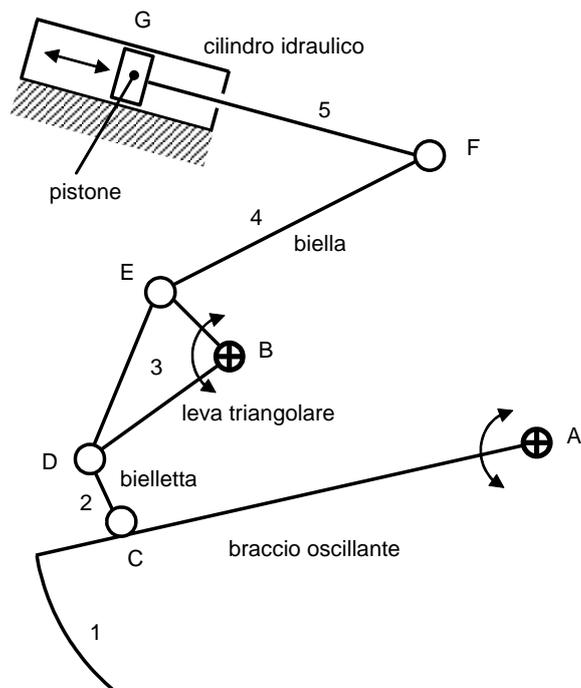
Catena cinematica di un meccanismo di Fig. 1.15
